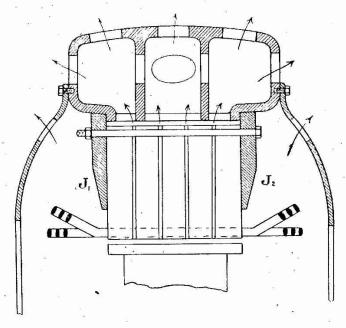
Coupe d'une carcasse avec les deux joues de serrage indépendantes. Enroulement à deux étages de bobines.
